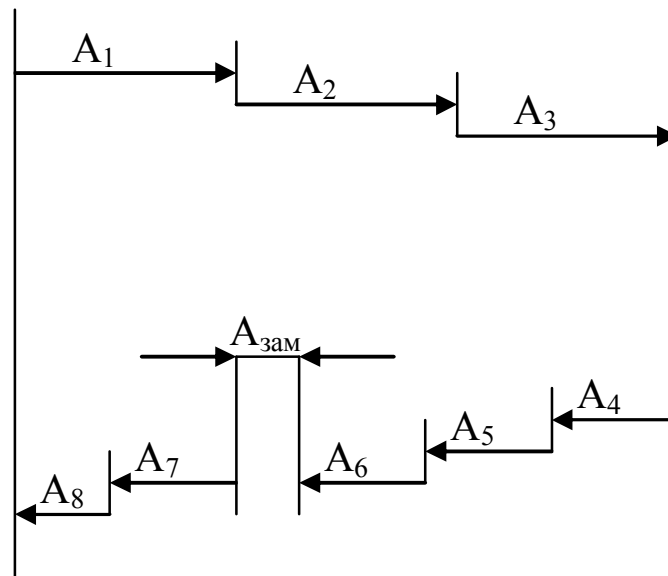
Схема розмірного ланцюга (→ – ланка, яка збільшує;
